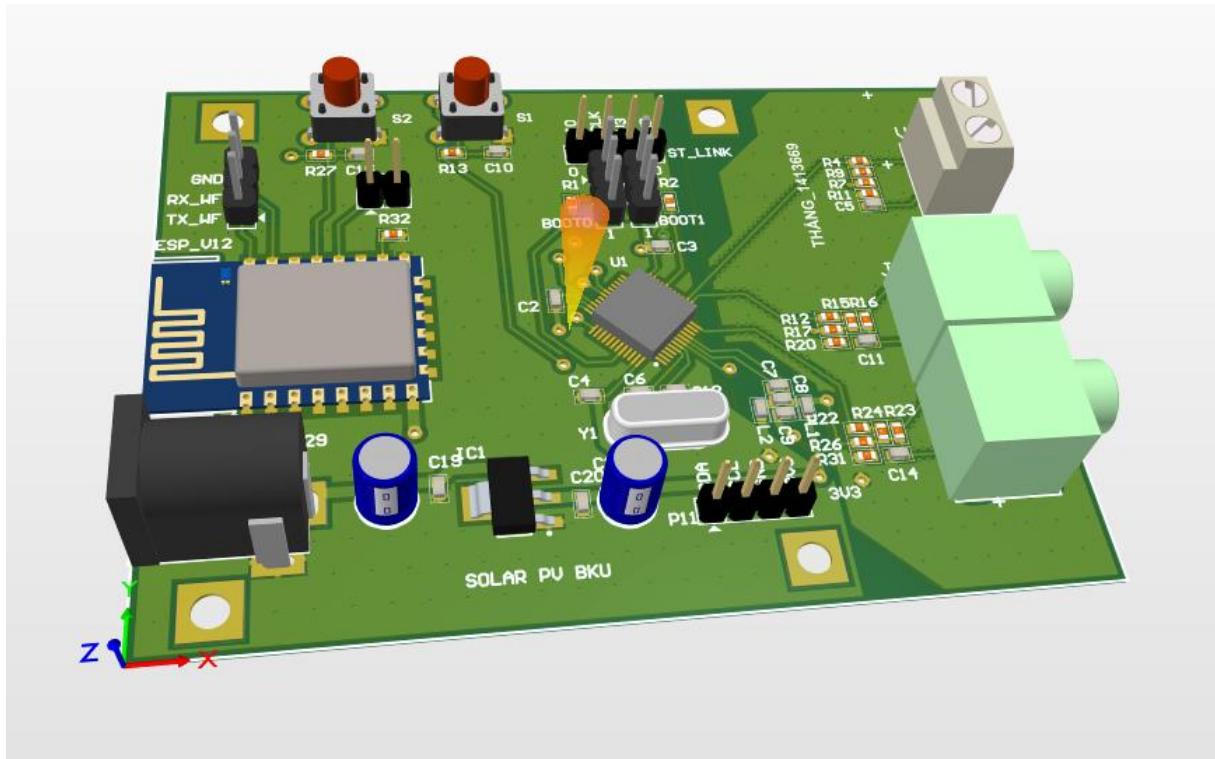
layout PCB mạch đo thông số ở điểm (1)
